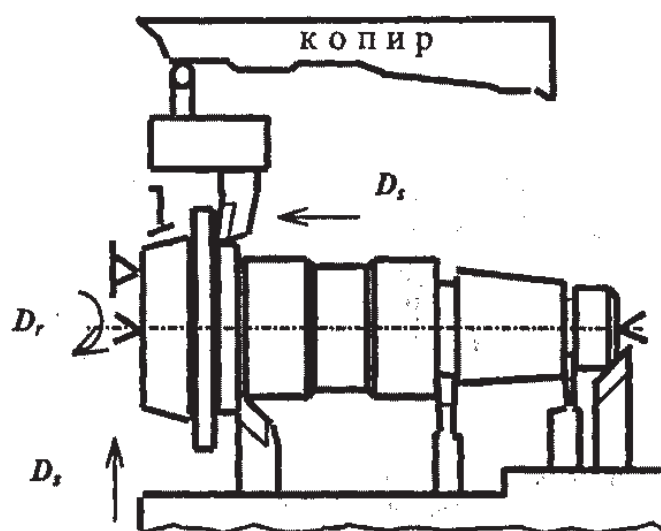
Схема обработки наружных поверхностей на токарном станке с гидроконтролируемым суппортом
